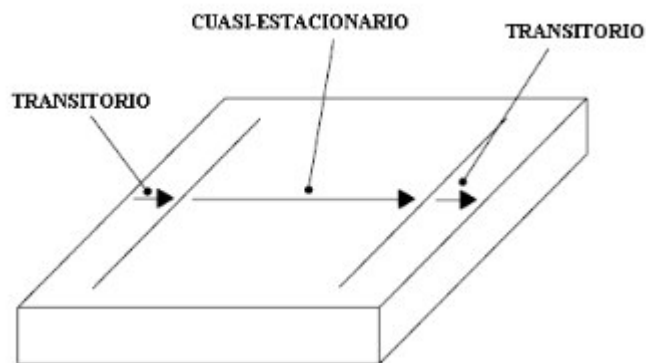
Etapas en el proceso de soldadura.
